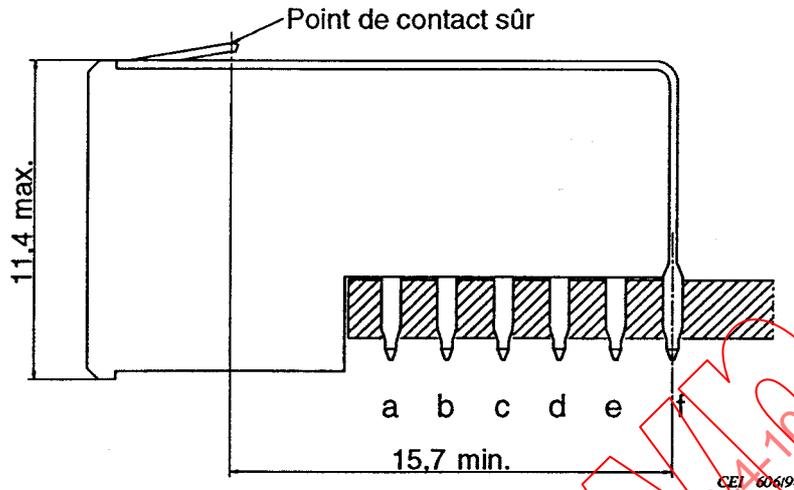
Dimensions d'accouplement de la coquille de blindage de la rangée f
